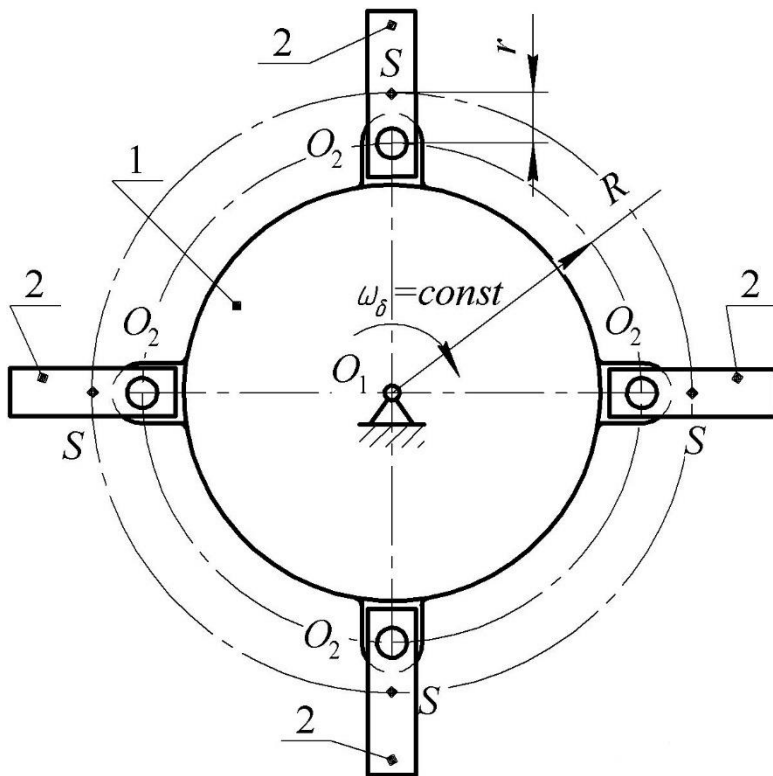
Схема агрегата с шарнирными рабочими элементами
